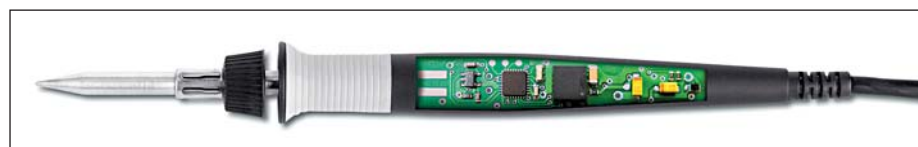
Встроенный контроллер в рукоятке паяльника i-Tool
